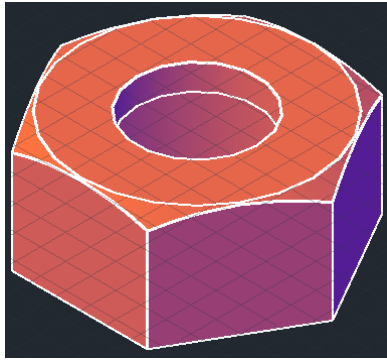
Готова 3D-модель гайки у середовищі AutoCAD
